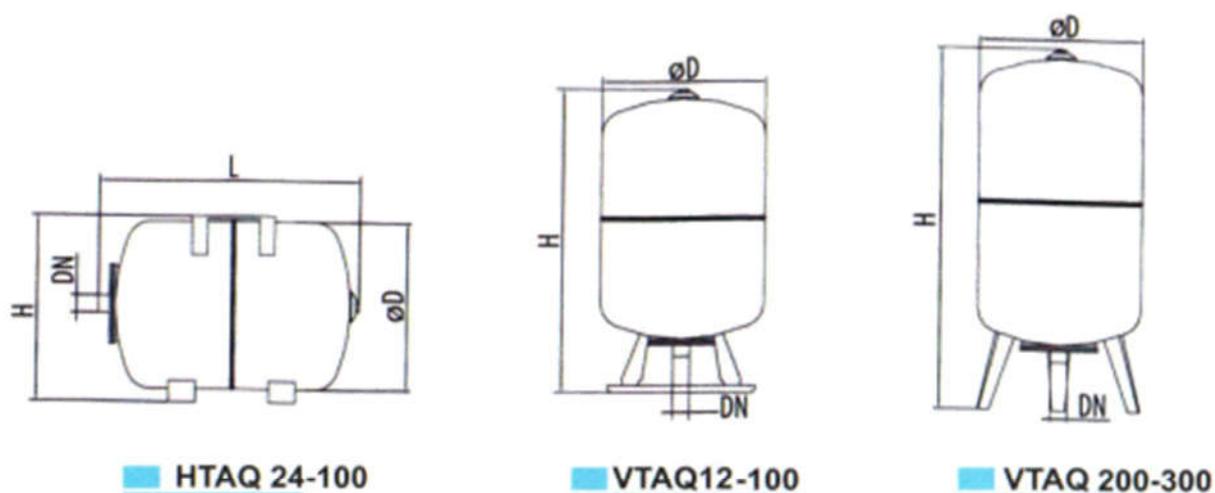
Габаритно-присоединительные размеры гидроаккумуляторов
